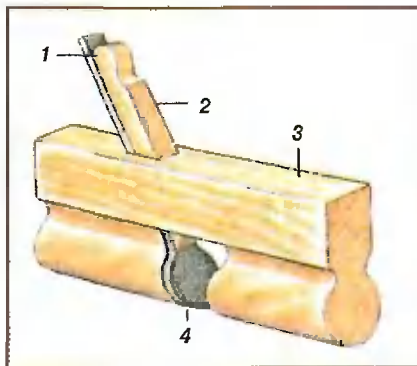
Галтель: 1 — нож; 2 — клин; 3 — колодка; 4 — лезвие ножа.
